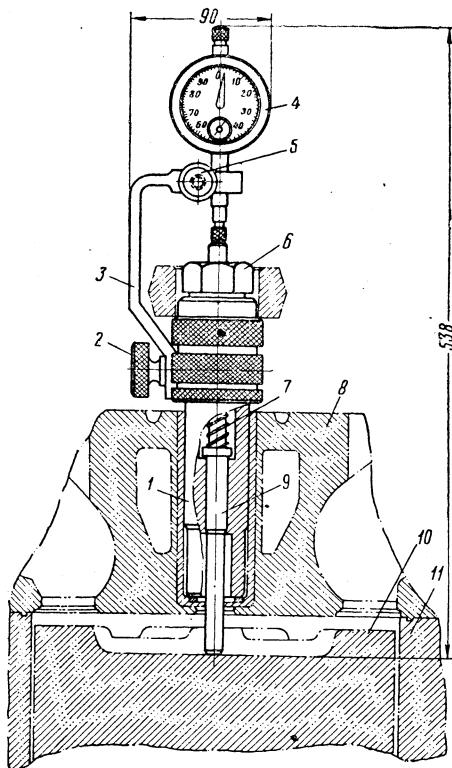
Приспособление (регляж) для проверки в. м. т. поршня дизеля 2Д50:
